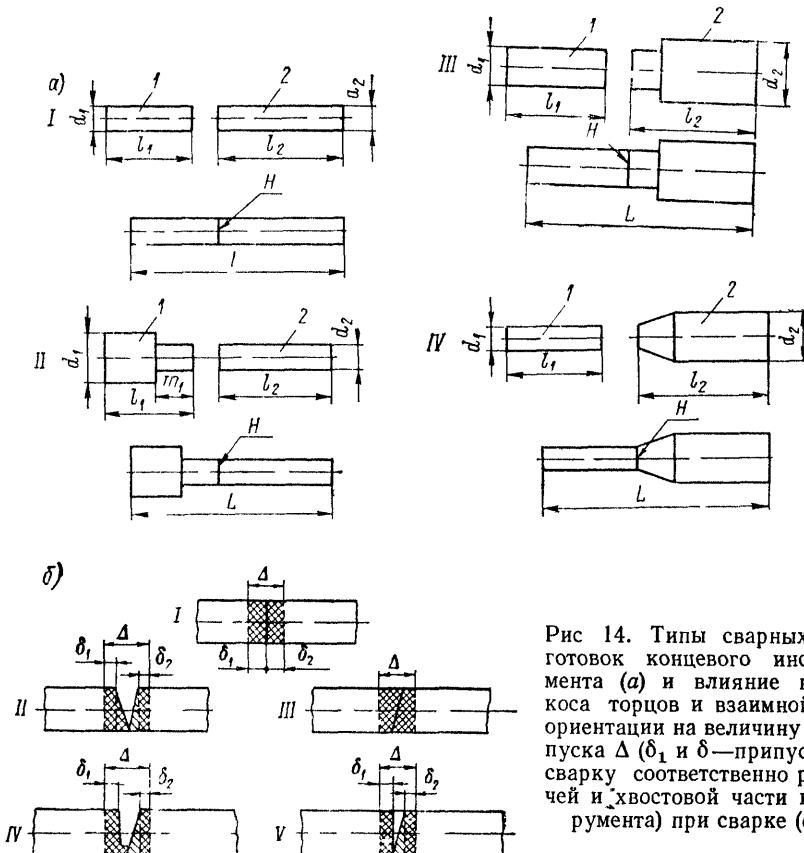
Типы сварных заготовок концевого инструмента (а) и влияние перекоса торцов и взаимной их ориентации на величину припуска Δ (δ_1 и δ —припуск на сварку соответственно рабочей и хвостовой части инструмента) при сварке (б)
